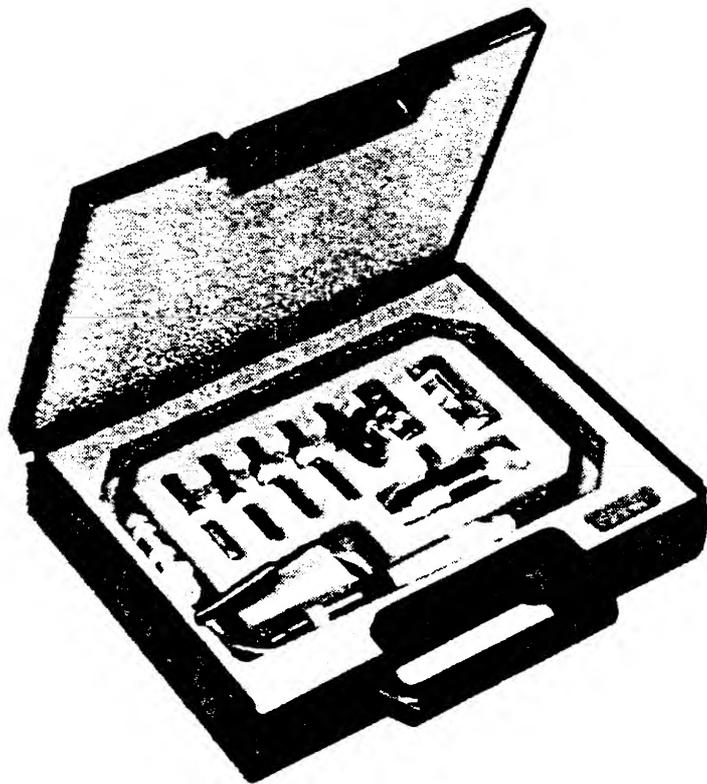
COFFRET D'ACCESSOIRES EQUIPE
